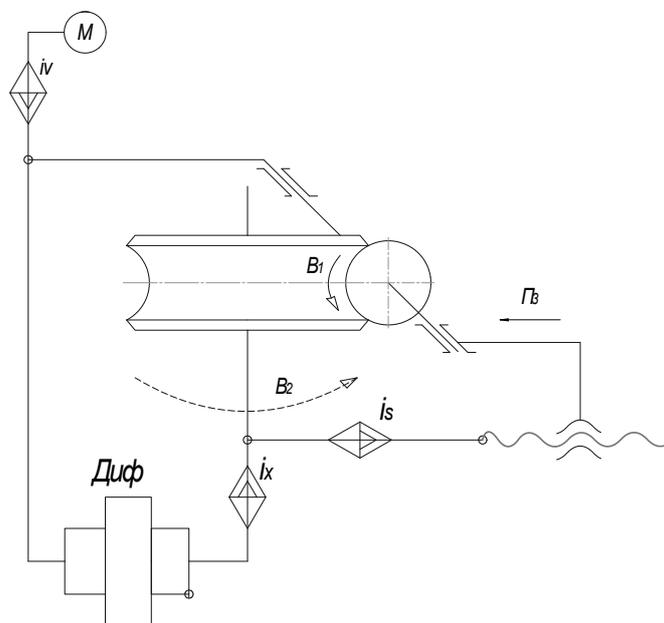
Кинематическая структура станка при нарезании цилиндрического прямозубого колеса
